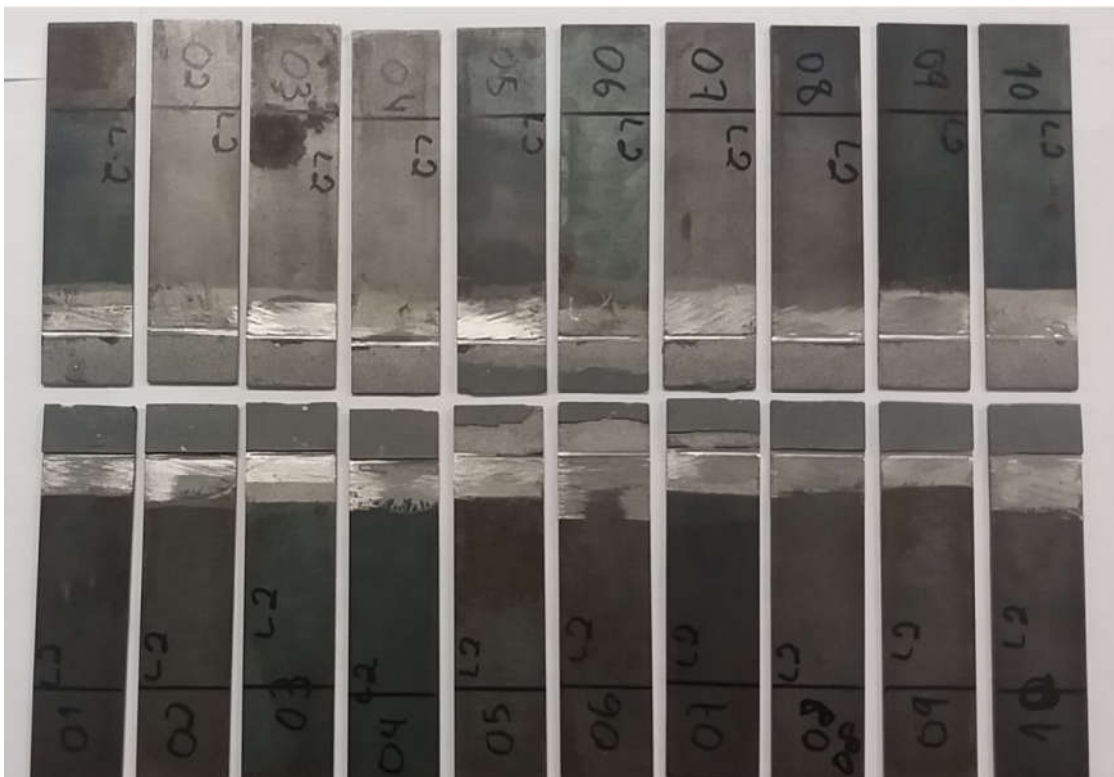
Juntas metálicas coladas com adesivo NVT 201E lote 1/0,5% NTC
